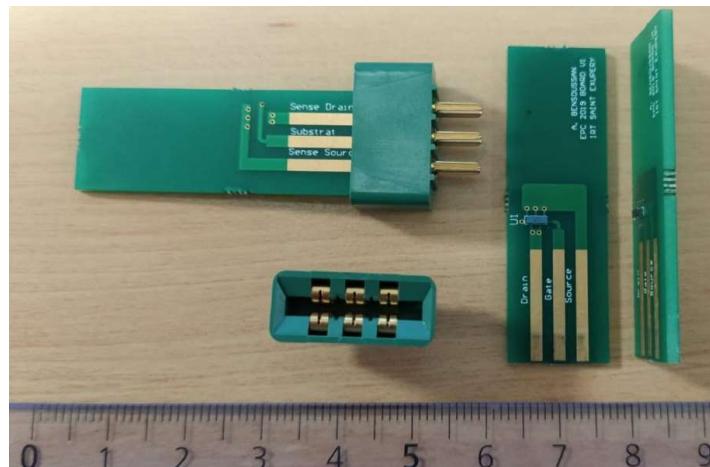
Composant sous test soudés sur les cartes PCB1 et des connecteurs
